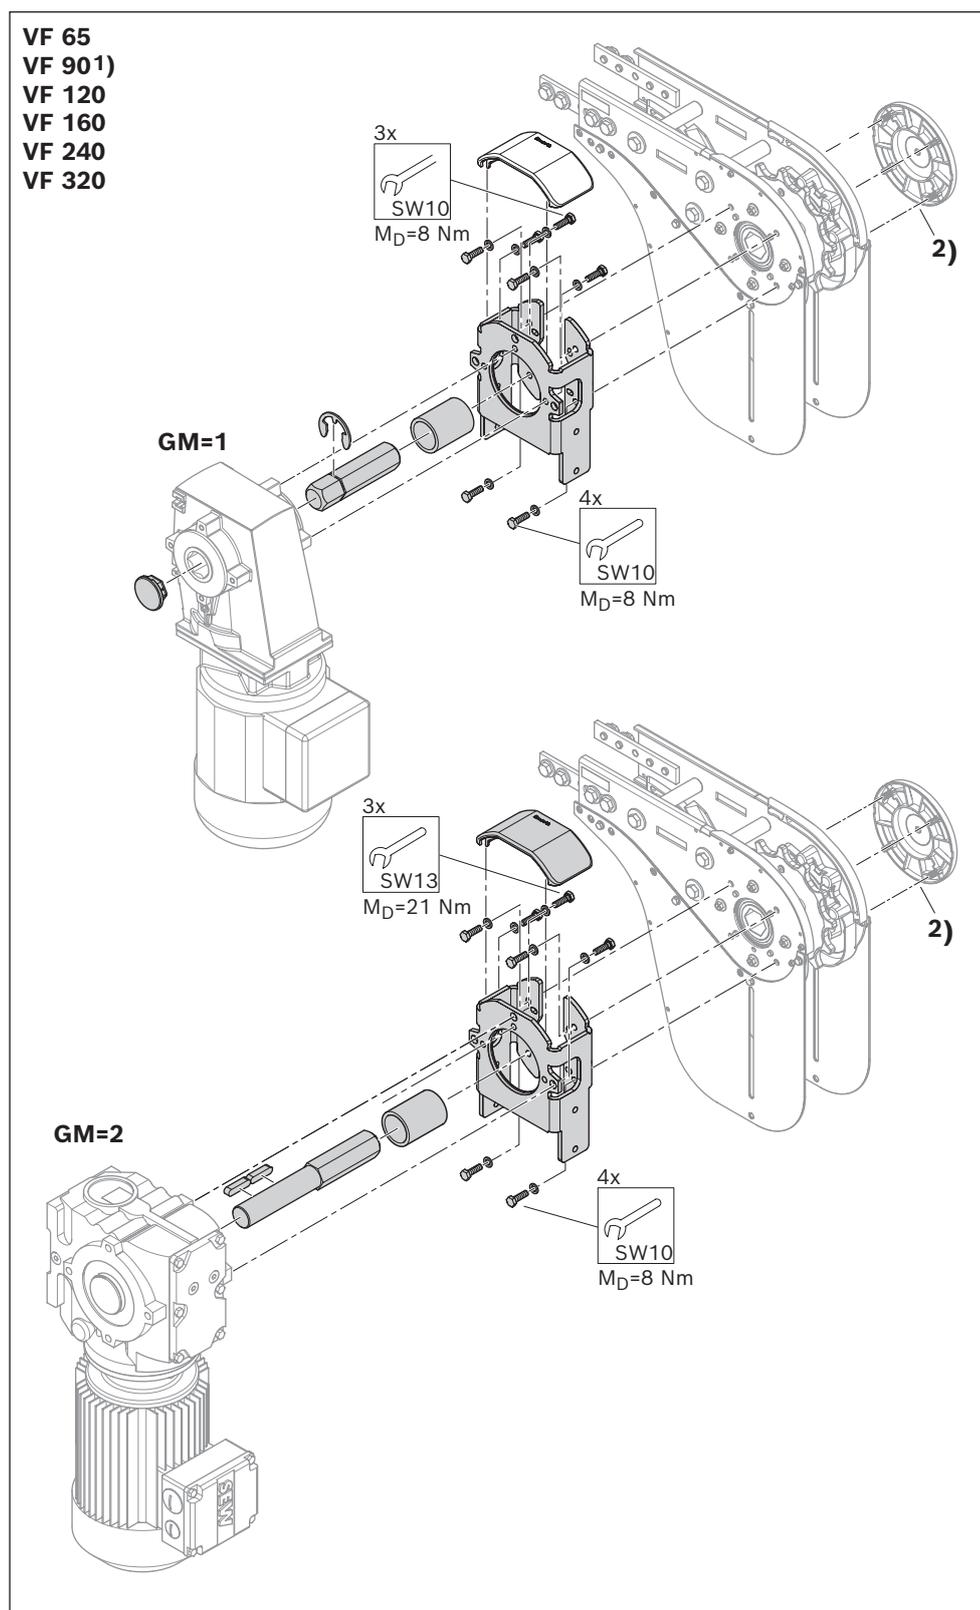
Montaje de la unidad básica, sistema STS, motor reductor
